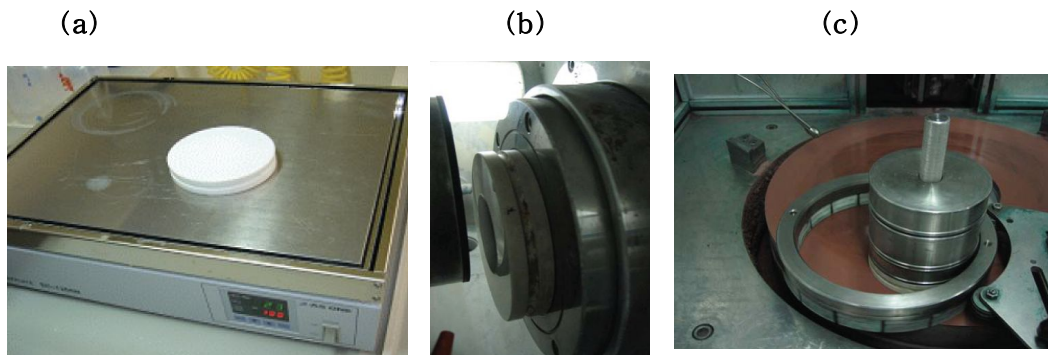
LED 후가공에 사용 되는 지그와 (a) hot plate, (b) Grinder machine, (c) Lapping machine
